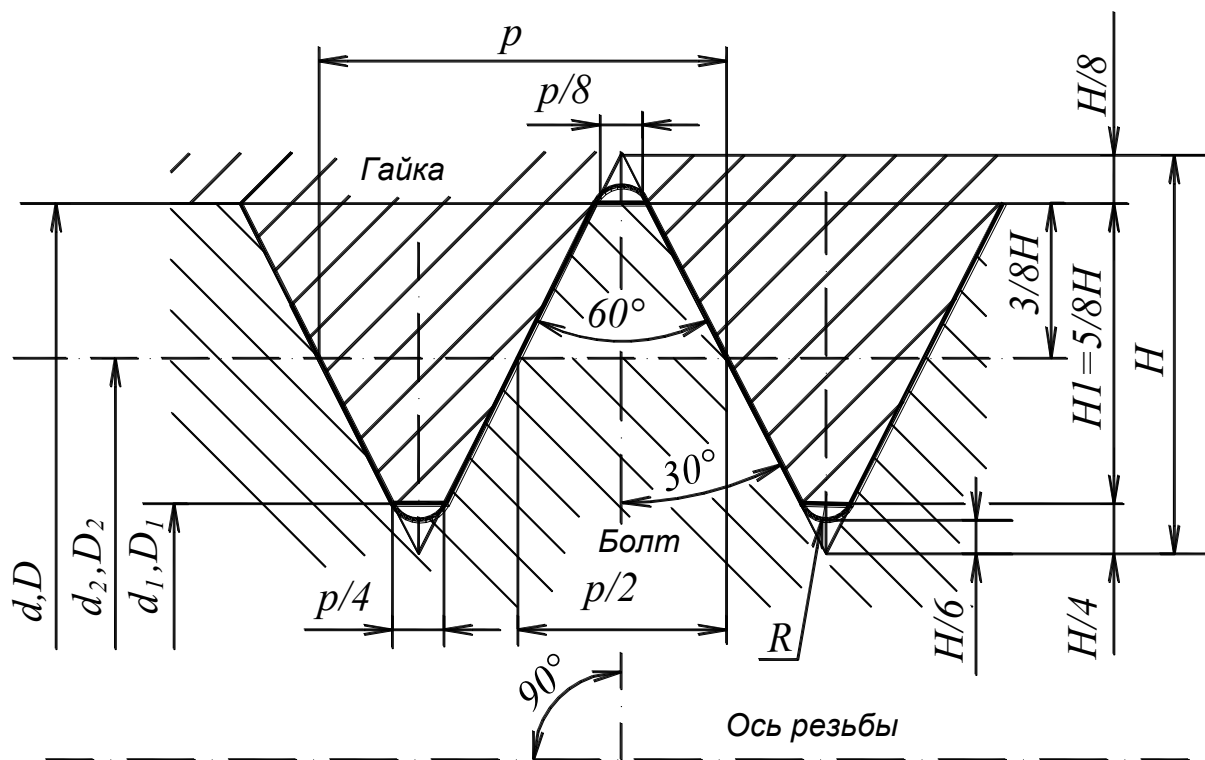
Профиль метрической резьбы и ее основные параметры
